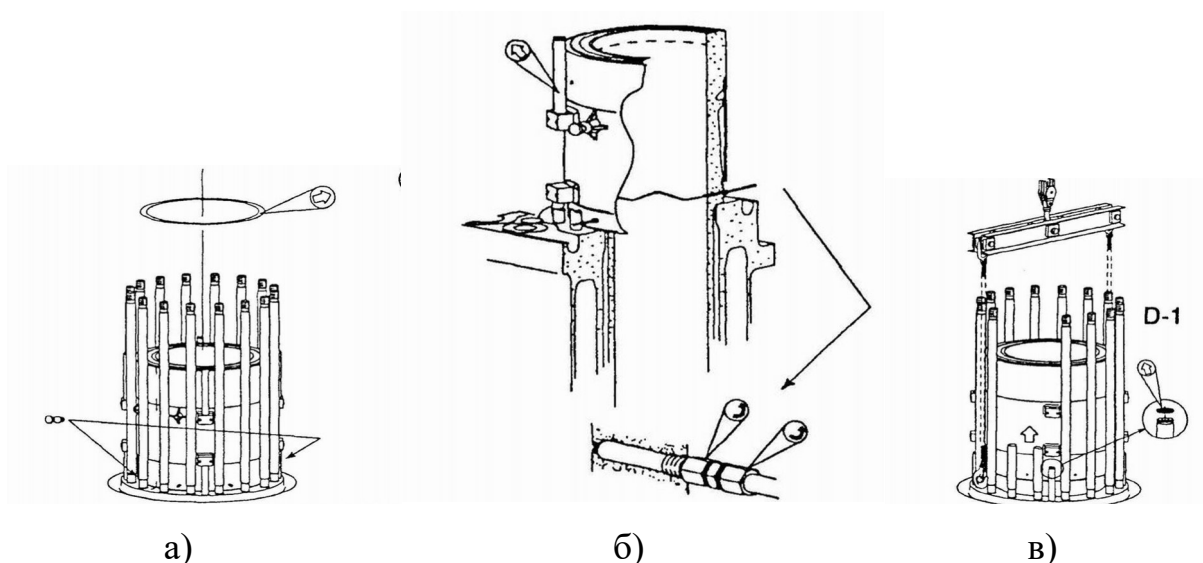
Демонтаж втулки з охолоджувальною сорочкою
